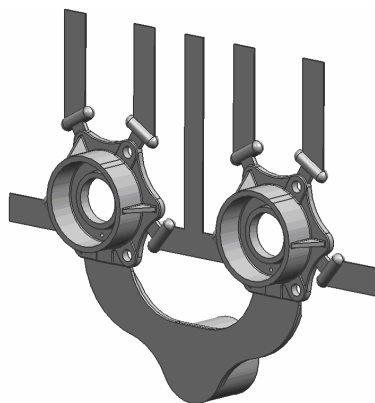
трехмерная модель отливки «Корпус 007»
